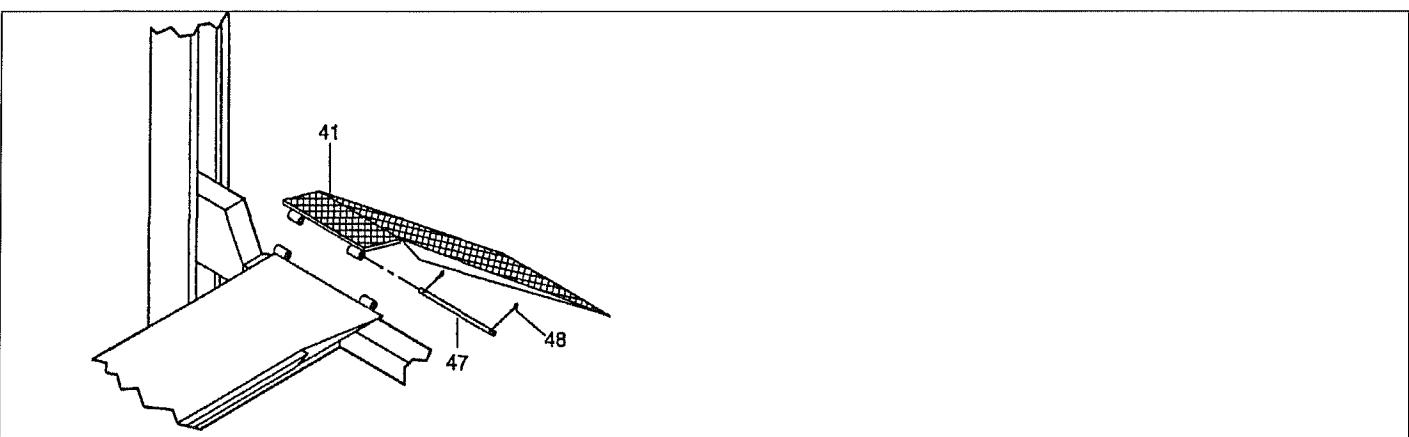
Крепление упоров колес и рамп заезда автомобиля
